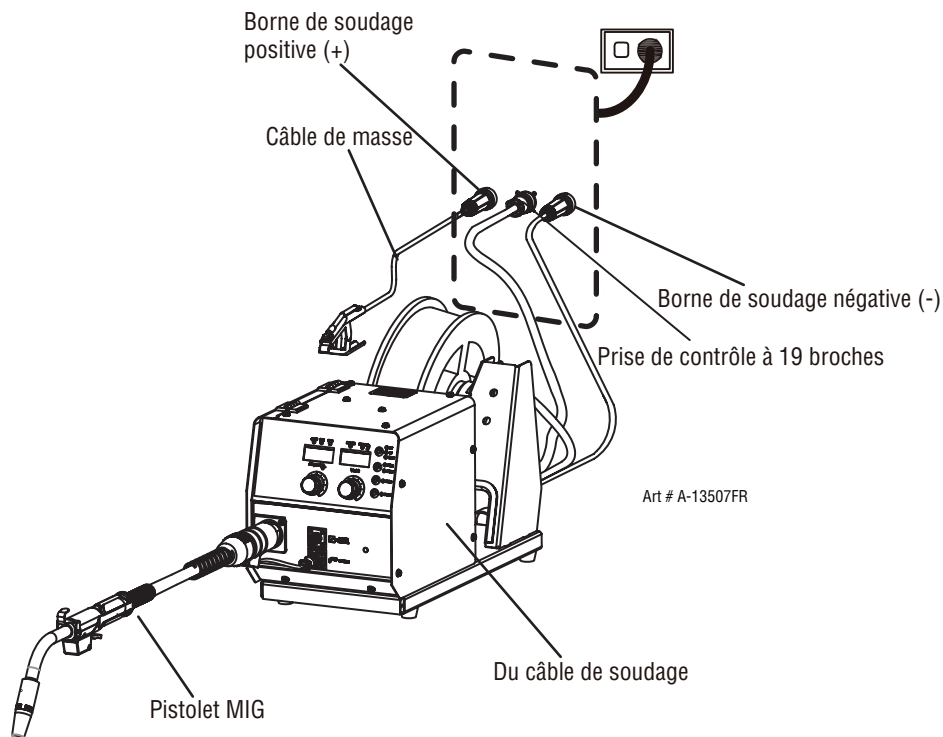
Configuration pour le soudage à l'arc avec fil fourré FCAW
